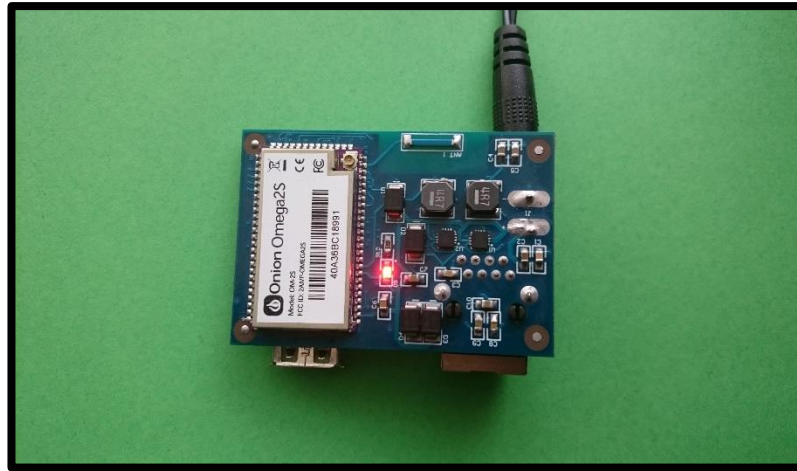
Vista superior del PCB con componentes. (elaboración propia)
